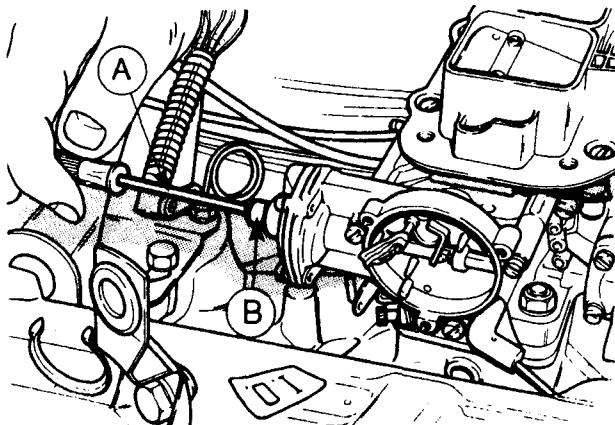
Регулировка хода заслонки под воздействием разрежения - карбюратор WEBER. А - Отвёртка. В - Корпус.
